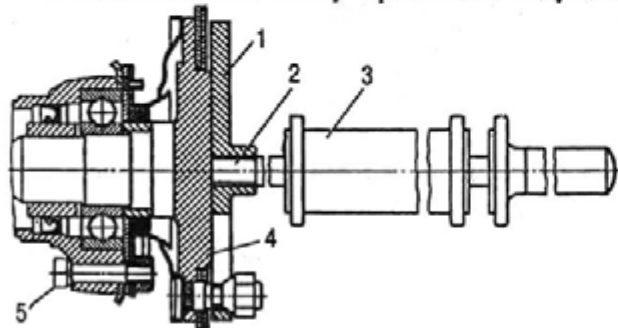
Выпрессовка полуоси при помощи приспособления 7823-6091:
